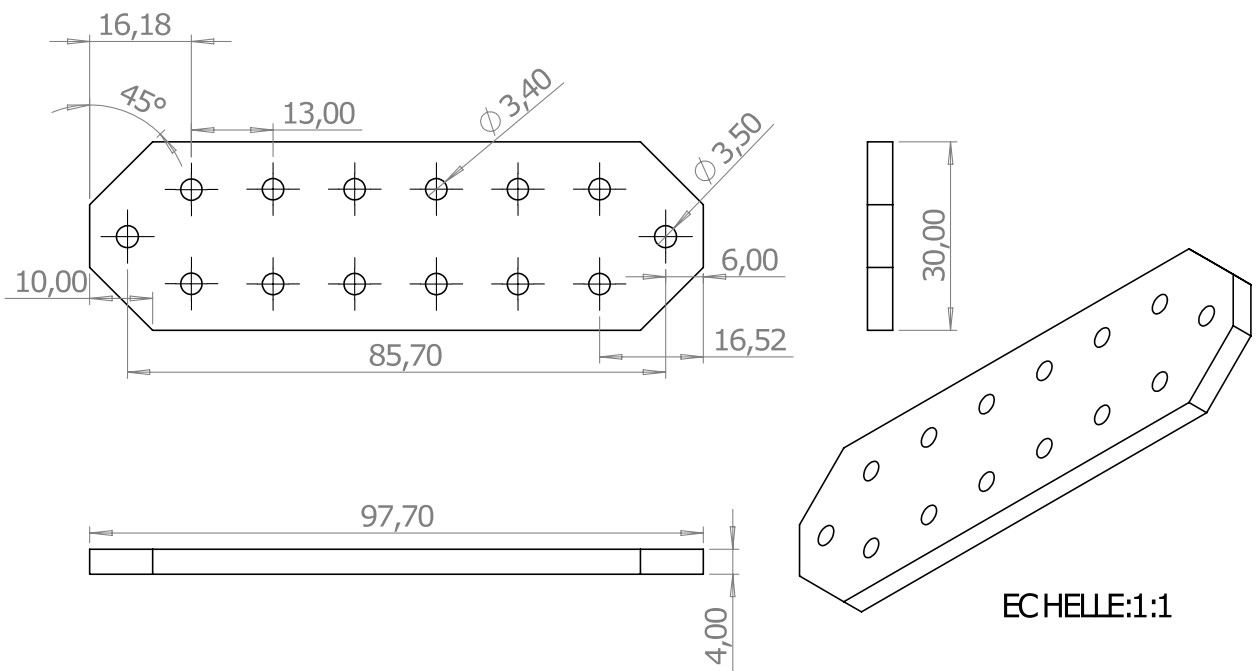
Dessin technique des plaquettes de fixation des bobinages moteurs
